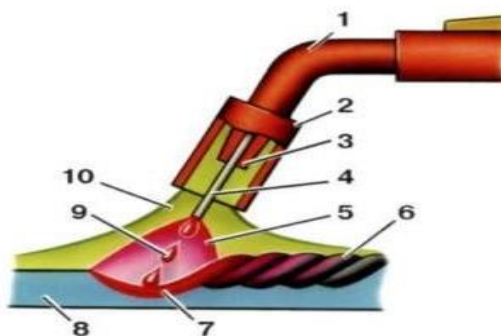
Эскиз механизированной сварки плавящимся электродом в смеси защитных газах
